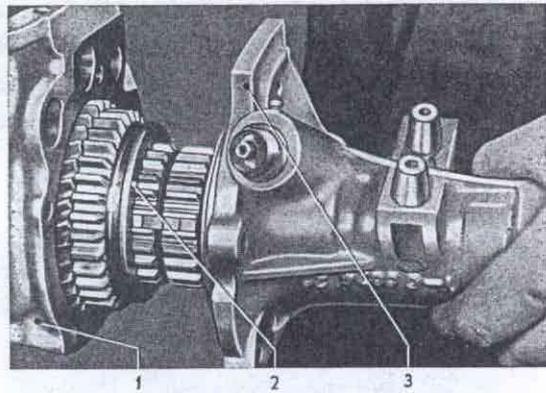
Getriebegehäuseverlängerung mit Hauptwellen-Zahnradblock aus Getriebegehäuse ausführen
